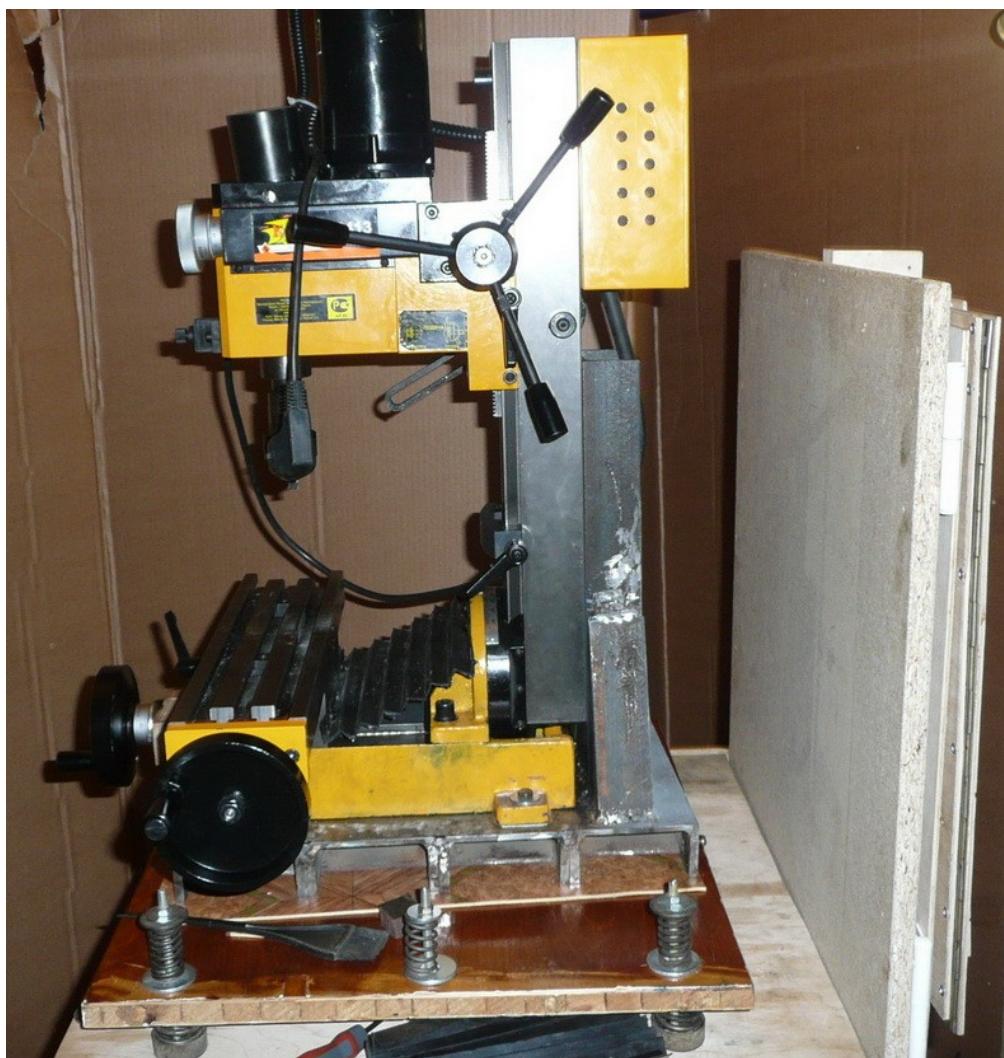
Станок фрезерный ЭНКОР Корвет 413 94130
